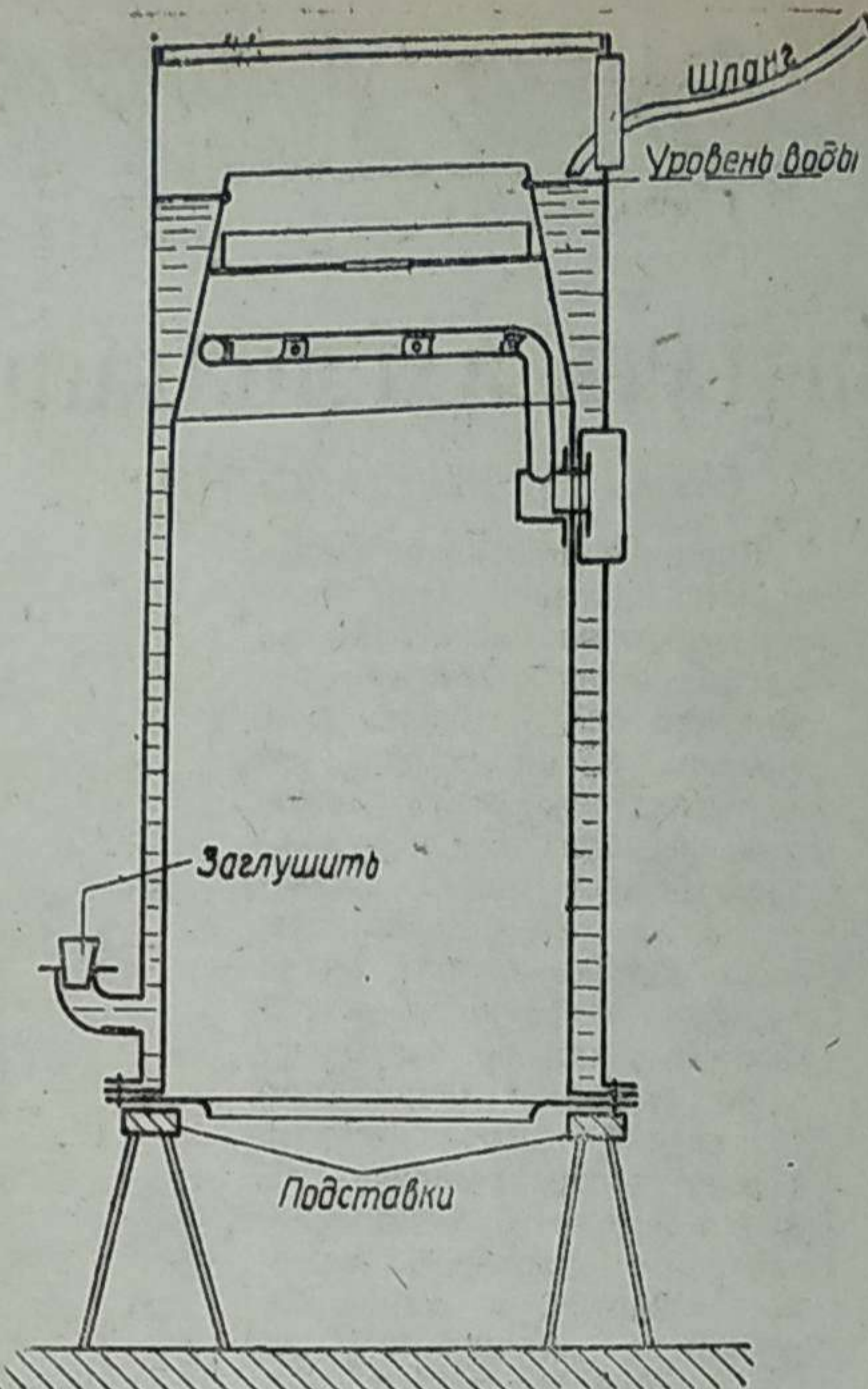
Установка газогенератора для проверки его герметичности при помощи заливки водой.
